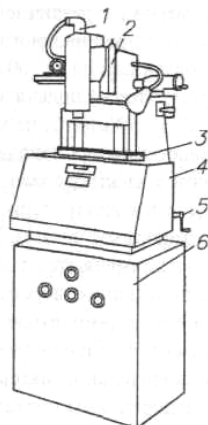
Общий вид универсального прошивочного станка для обработки заготовок массой до 10 кг: 1 – регулятор подачи электрода-инструмента; 2 – электродержатель; 3 – рабочий стол; 4 – рабочая ванна; 5 – ручной механизм подъема ванны
